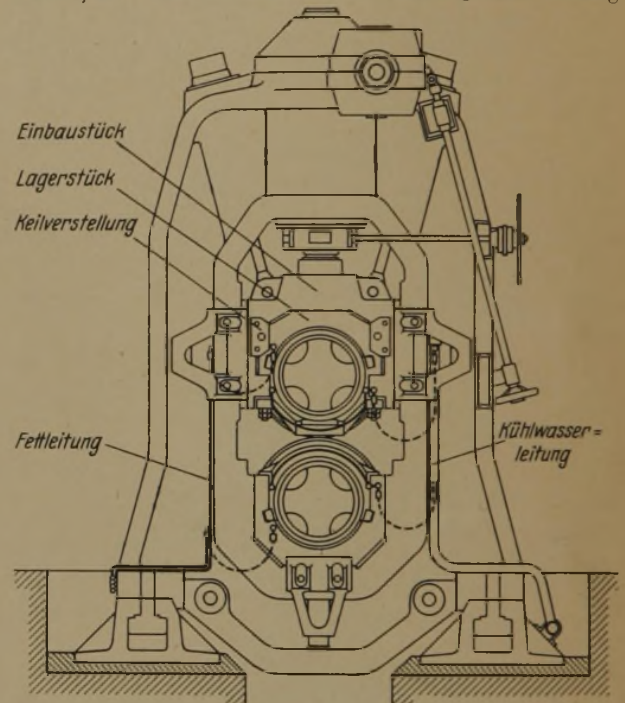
Zweiwalzgerüst mit seitlich verstellbarem Lagerstück für die Oberwalze.
